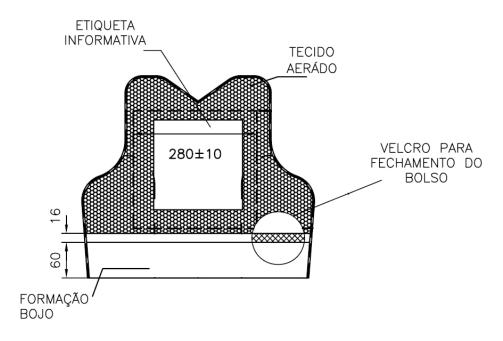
CAPA FRONTAL, FACE INTERNA
